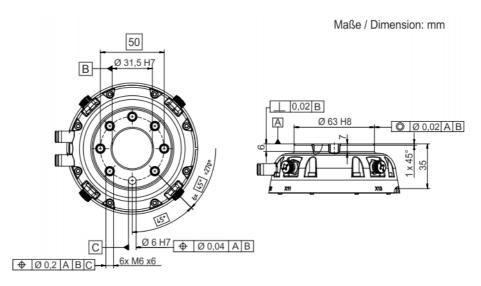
Abmessung, Medien-Flansch IO pneumatisch
